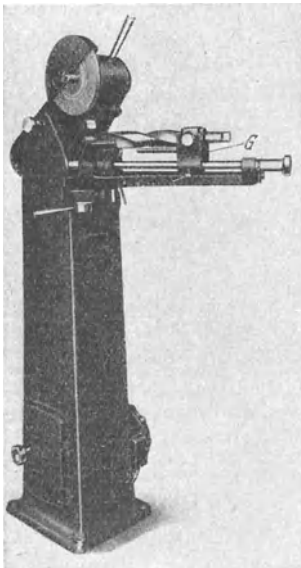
Spiralbohrer-Ausspitzmaschine.
